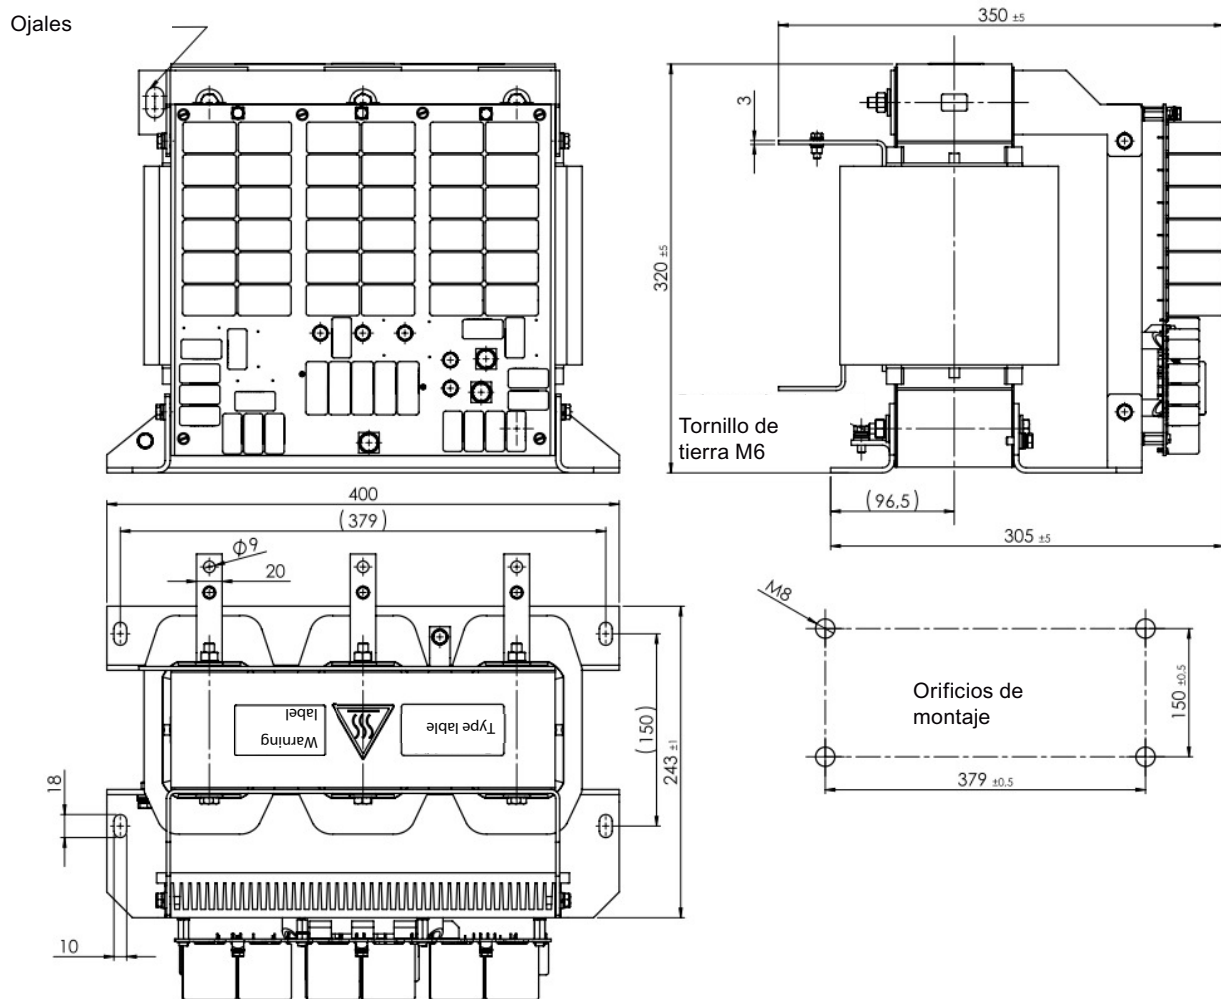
Dimensiones de JTA:TEF1203-0LB
